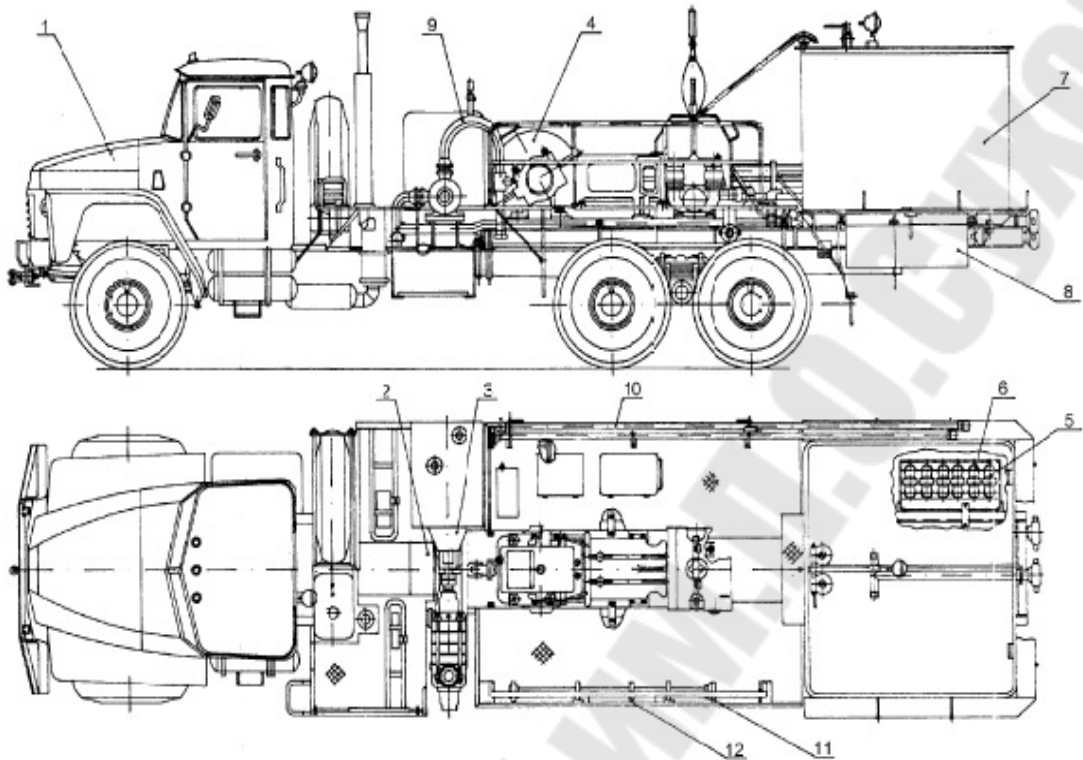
Конструкция цементировочного агрегата: 1 – шасси автомобиля; 2 – коробка отбора мощности; 3 – блок водоподающий с центробежным насосом; 4 – насос; 5 – колено шарнирное; 6 – колено шарнирное сдвоенное; 7 – бак мерный с донными клапанами; 8 – бачок цементный; 9 – манифольд
